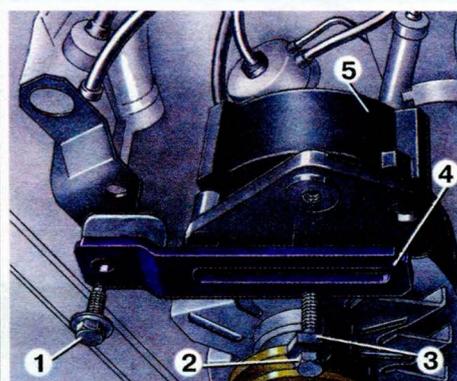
Крепление механизма натяжения генератора 4-цилиндрового бензинового двигателя: 1 – болт крепления кронштейна механизма натяжения ремня; 2 – болт механизма натяжения ремня; 3 – гайка механизма натяжения ремня; 4 – кронштейн механизма натяжения; 5 – генератор
